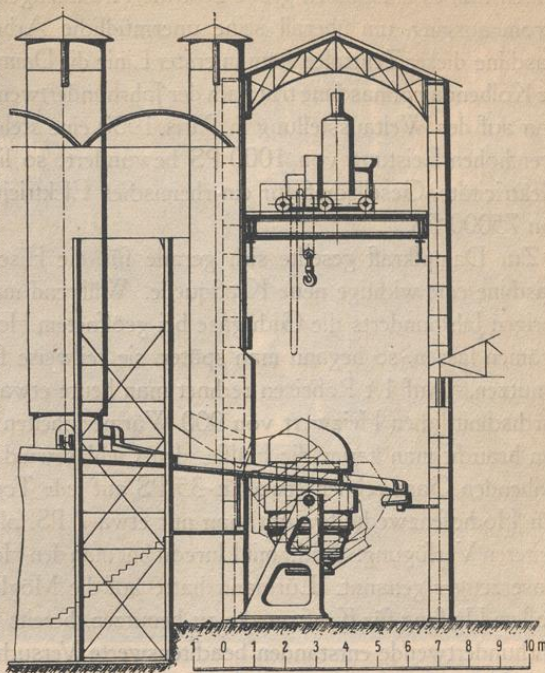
Mit Dampf betriebener Laufkran im Stahlwerk Hayingen. Nach einer Zeichnung aus dem Jahre 1879 aus dem Nachlaß von Alfred Trappen.
